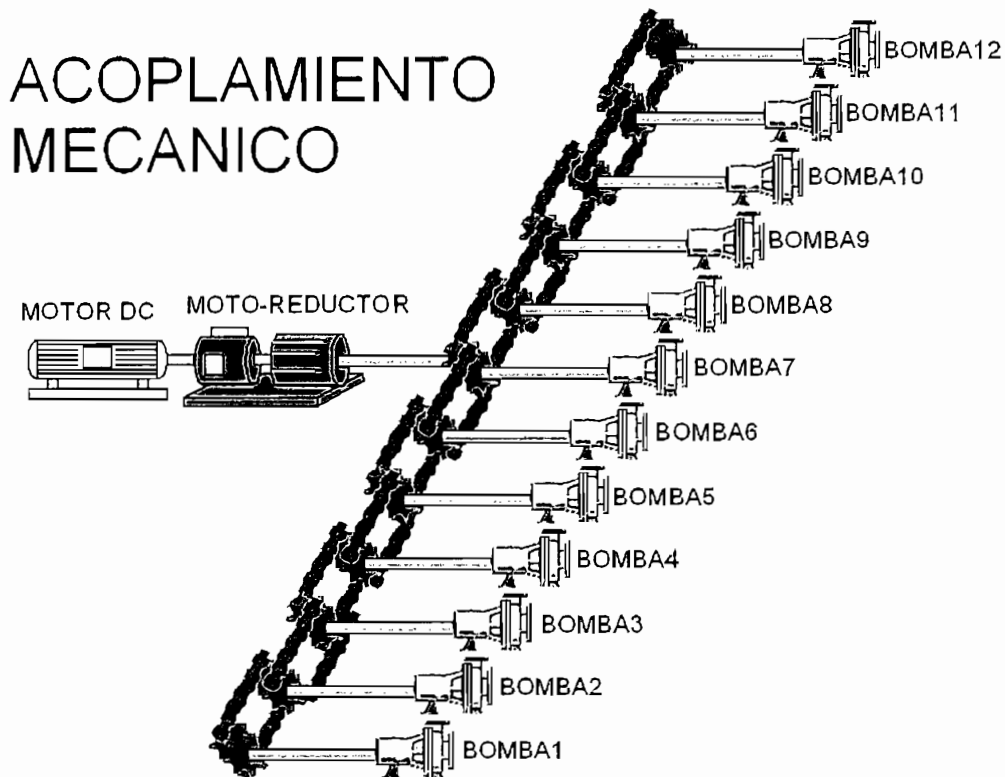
Acoplamiento mecánico del motor con las bombas
